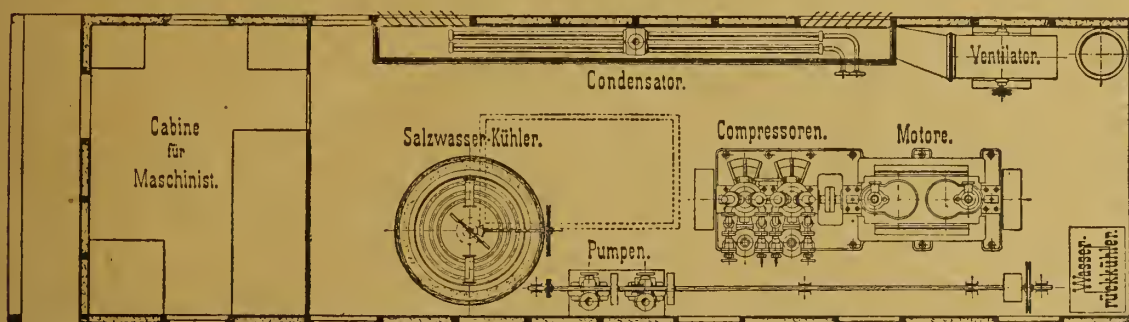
Maschinenkühlwagen der Ges. für Lindes Eismaschinen.
